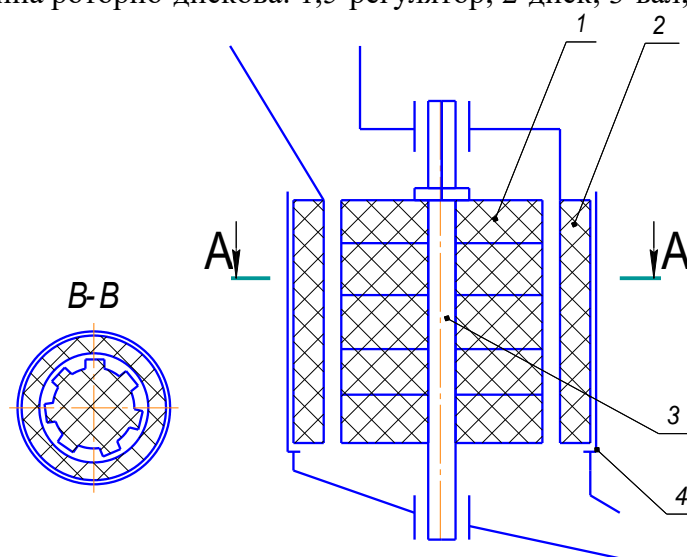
Машина роторно-вальцева: 1-циліндр; 2-валець; 3-вал; 4-корпус.
